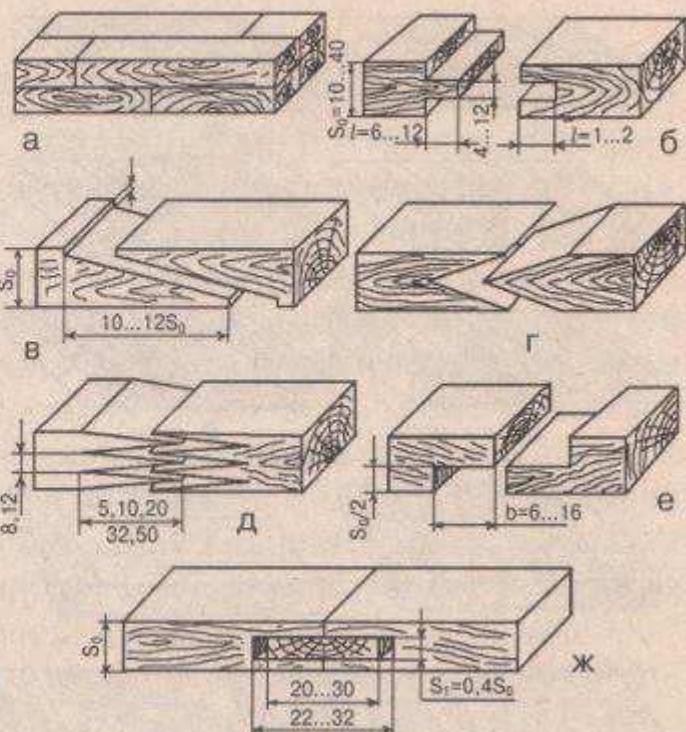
Соединения брусков по длине: а — впритык; б — в паз и гребень; в — на «ус»; г, д — на зубчатое kleевое соединение; е — в четверть; ж — на рейку
